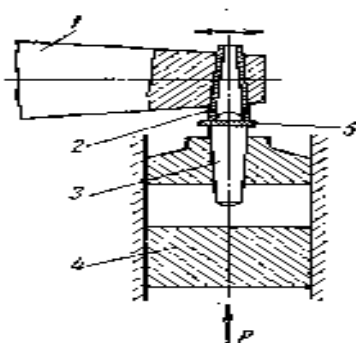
Схема ультразвуковой сварки
